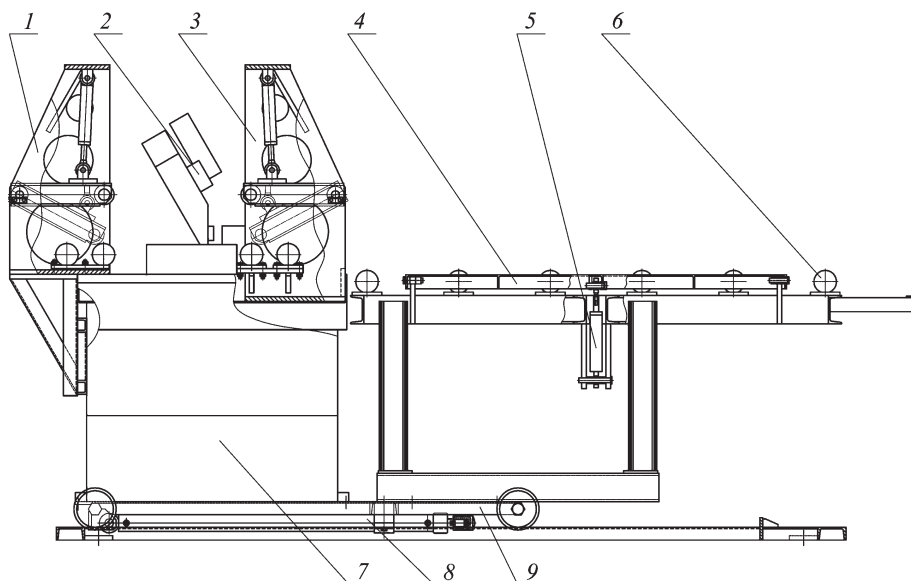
Общий вид механизма разделения заготовок: 1, 3 – прижимы; 2 – пильная рама; 4 – опрокидыватель; 5 – привод опрокидывателя; 6 – ролик; 7 – корпус ленточнопильного станка; 8 – привод механизма возврата; 9 – подвижное основание
